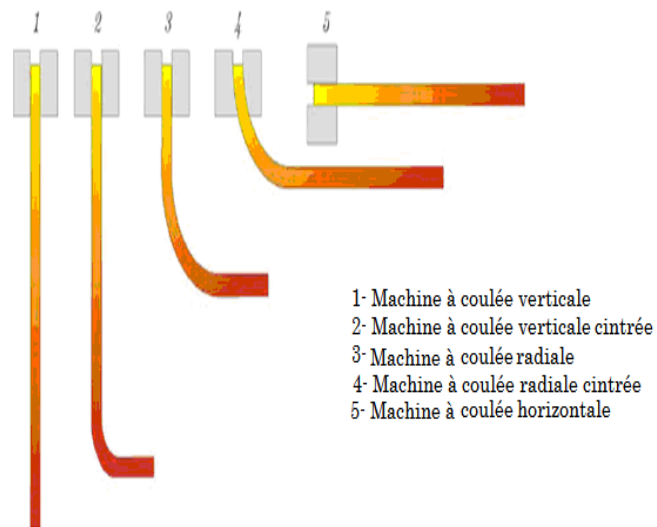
Différentes géométrie de machine de coulée continue [6].
